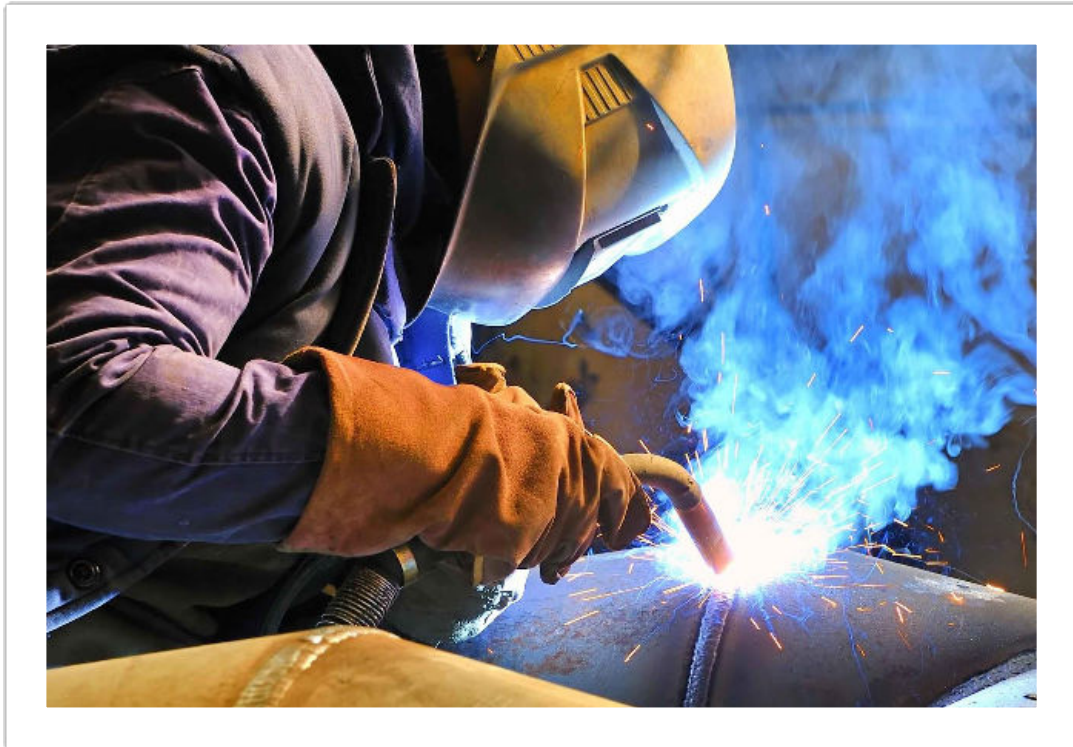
Puesto de Soldador Método REBA
